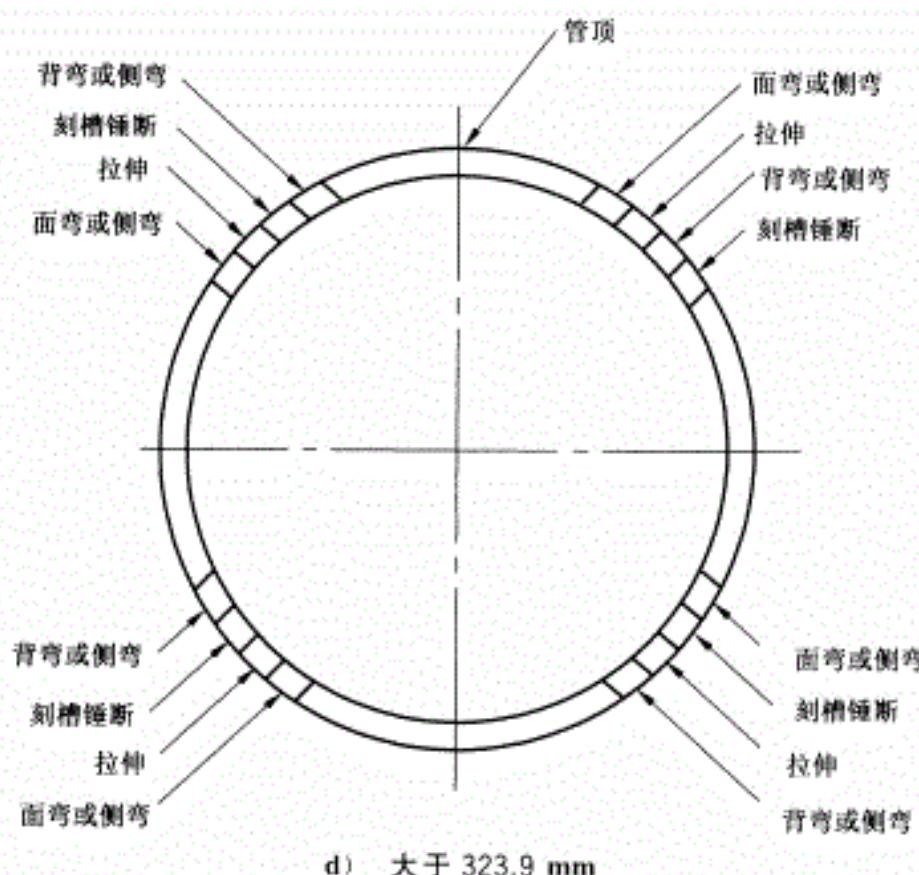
对接接头焊接工艺评定试验的试样位置
